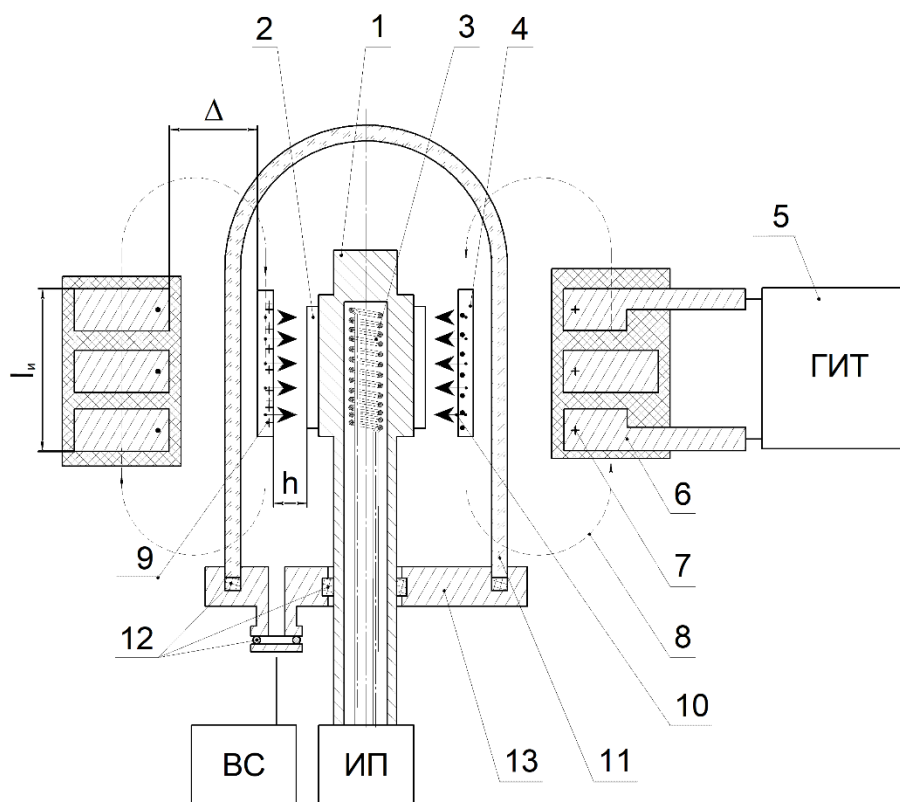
Схема устройства импульсной диффузионной сварки в вакууме:
